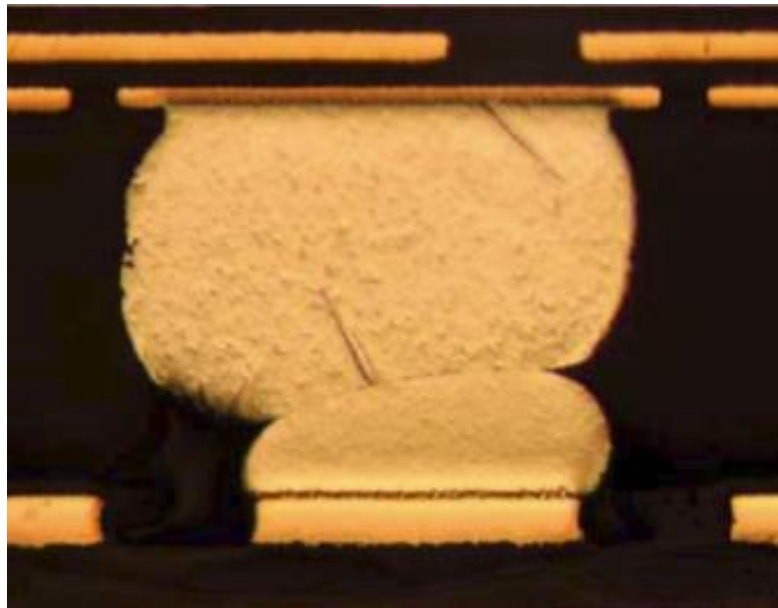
Defekt BGA – black pad efekt (přerušené spojení) (převzato z [29])
